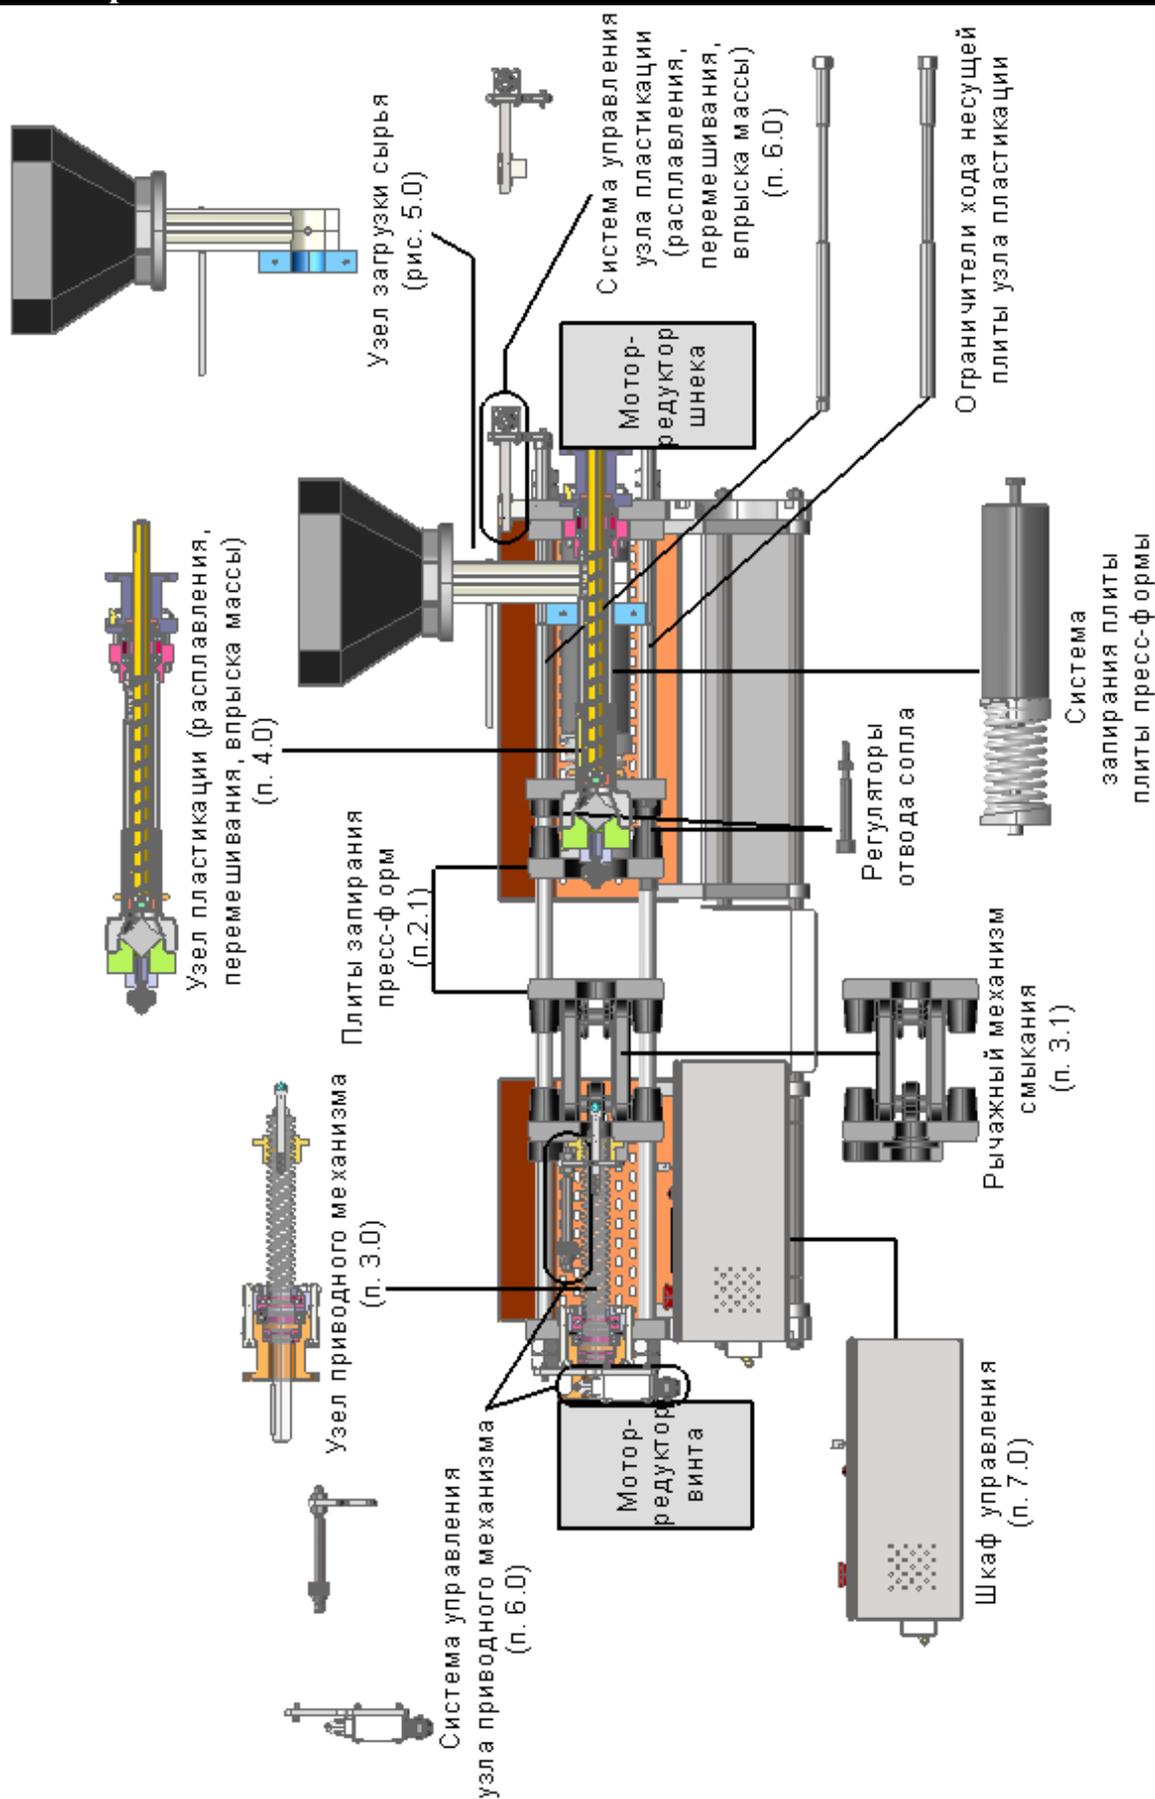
Устройство станка «Formolder IMS-55», «Formolder PRO 110/150»
